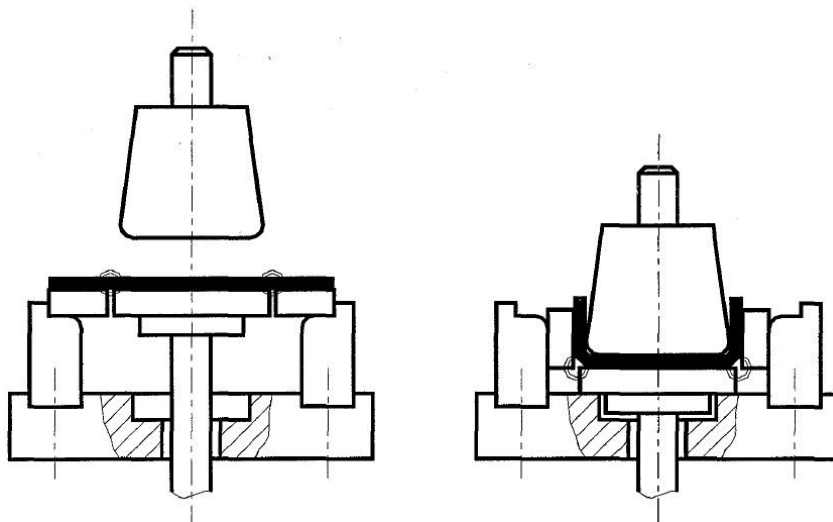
Схема двухугловой гибки с шарнирным соединением гибочных инструментов
